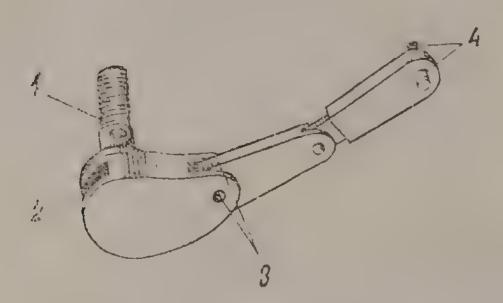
Барабан с цепочкой; 1 — винт барабана; 2 — паз для цепочки; 3 — ушки с отверстиями лля оси; 4 — шпилька для соединения с крючком возвратиой пружины
